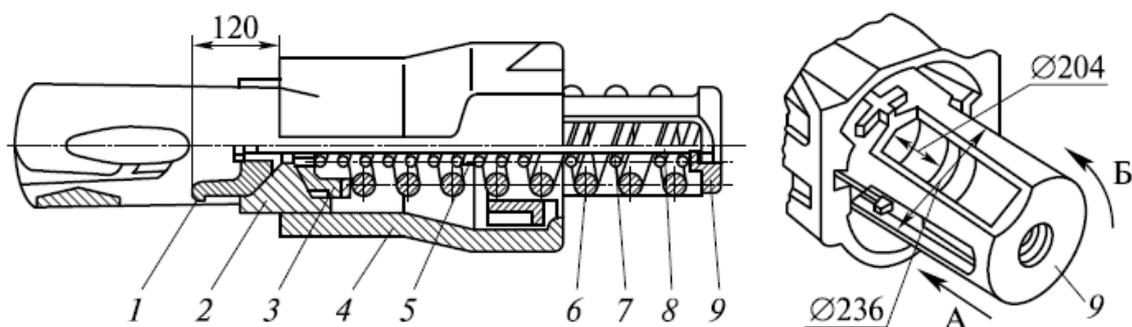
Аппарат Ш-6-ТО-4: общий вид; б - узел соединения корпуса с крышкой
